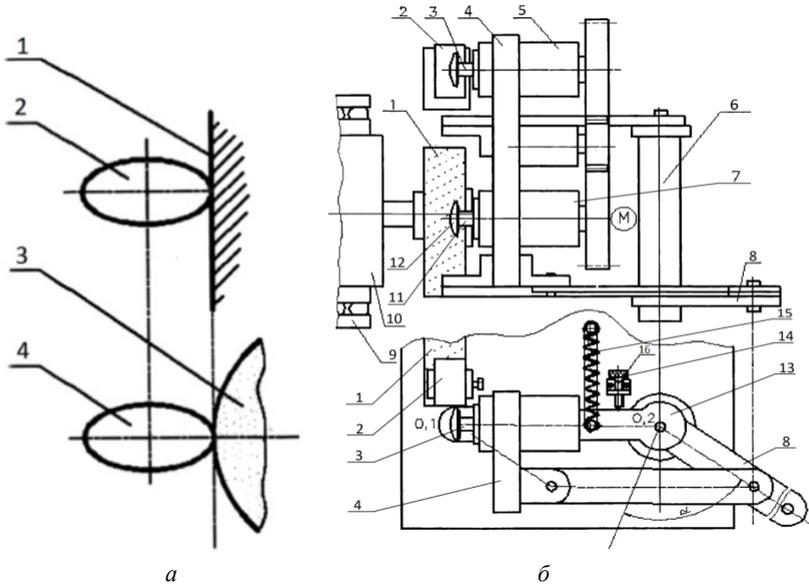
Схема копирующей обработки овального кабошона (а) и станка с механизированной подачей заготовки (б)
